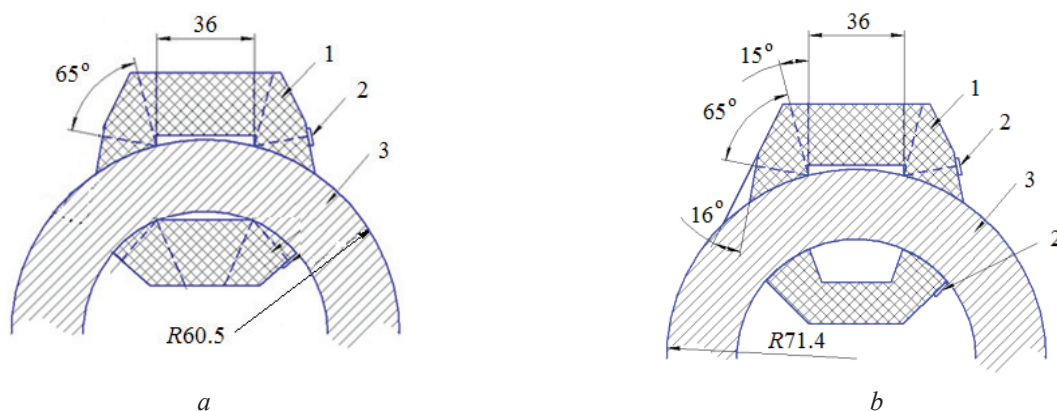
Рэлеевские преобразователи для контроля структурного состояния пружин радиусом 60,5 мм (a) и 71,4 мм (b): 1 – корпус преобразователя из оргстекла; 2 – пьезоэлемент; 3 – пружина
